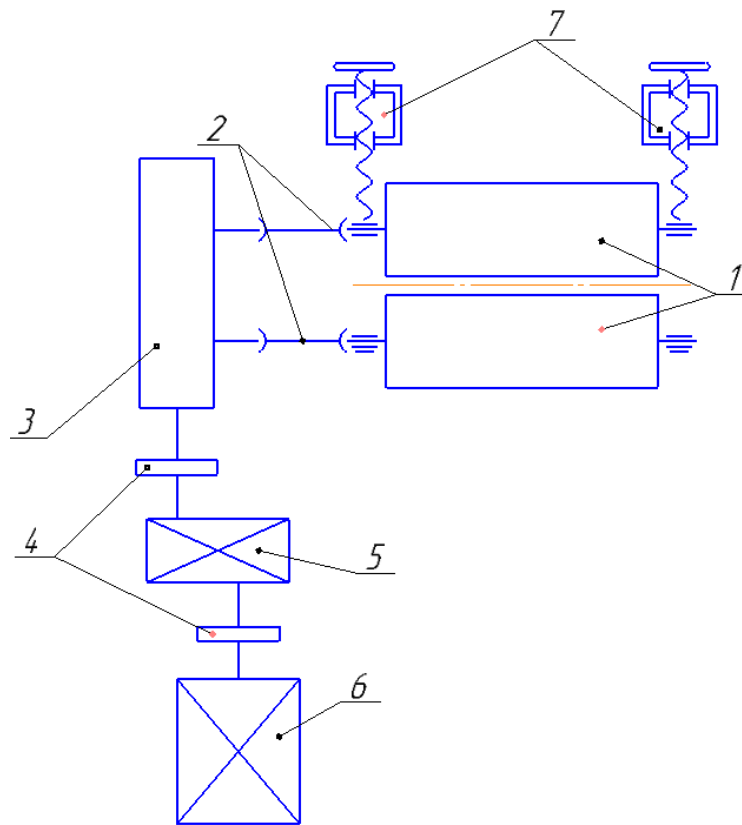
Кинематическая схема привода установки непрерывного литья
